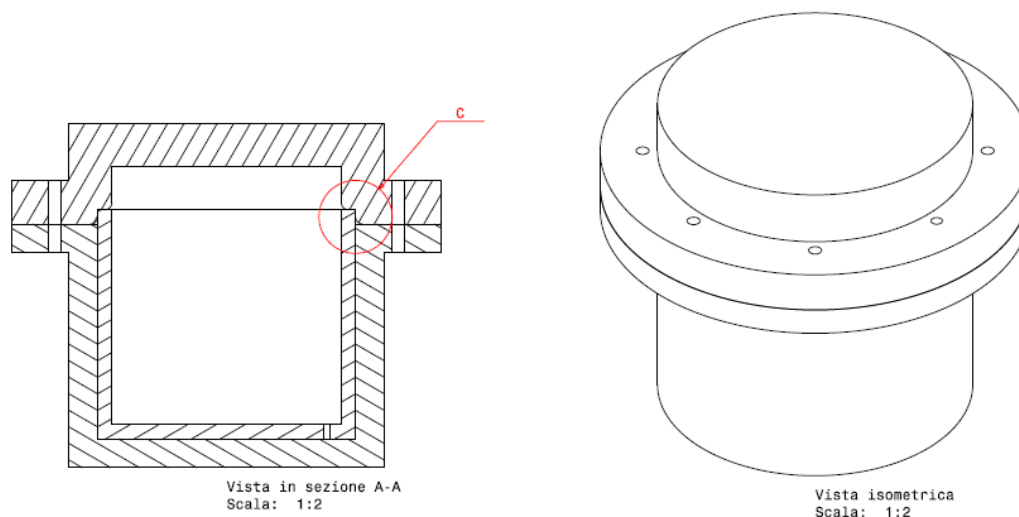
Vista in sezione per evidenziare il risalto e vista isometrica.
